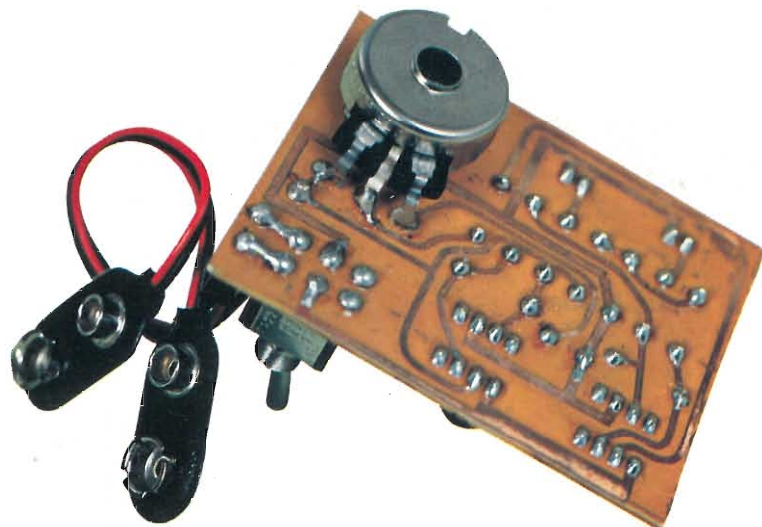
Vista dello stampato MK080 dal lato rame; si noti il particolare montaggio del potenziometro.
